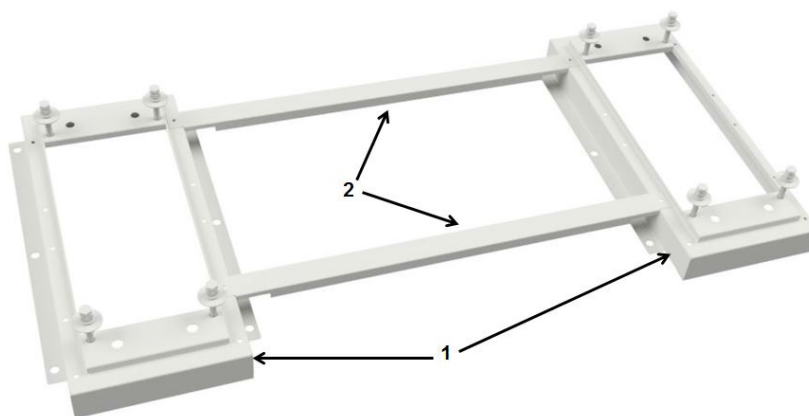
Samlet fixtur monteret med afstandsskinner
